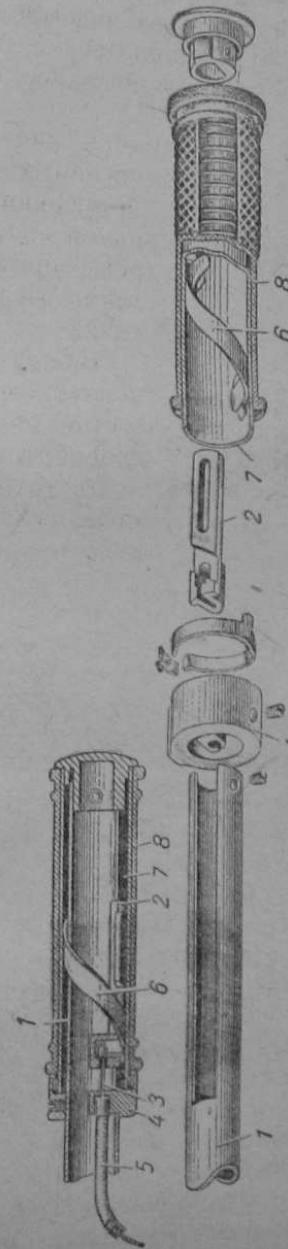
Вращающаяся рукоятка ползункового типа (М1А):
